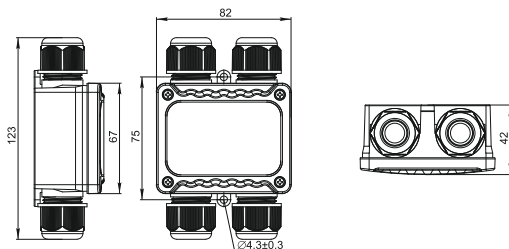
Габаритные размеры коробки WTP-403 / Figure 3 – Overall dimensions of the WTP-403 box
